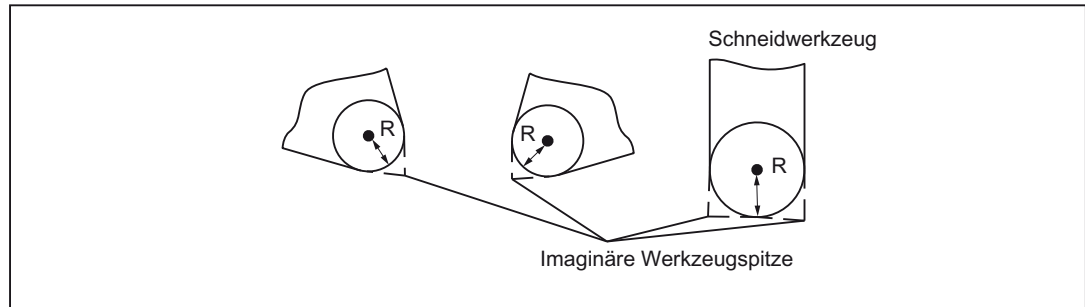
Festlegen des Betrages der Schneidenradiuskompensation und einer imaginären Werkzeugspitze
